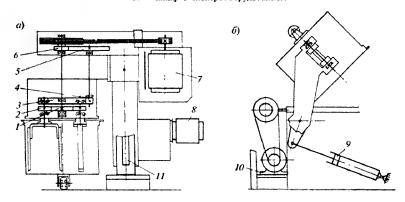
Кинематическая схема смесительной машины модели АПАМ-300: a — рабочее положение; δ — положение при разгрузке; I- δ — шестерии привода лопастей; S — электродвигатель протирочного устройства; θ — электродвигатель привода лопастей; $I\theta$ — станина; II — гидроцилиндр поворота чаши
